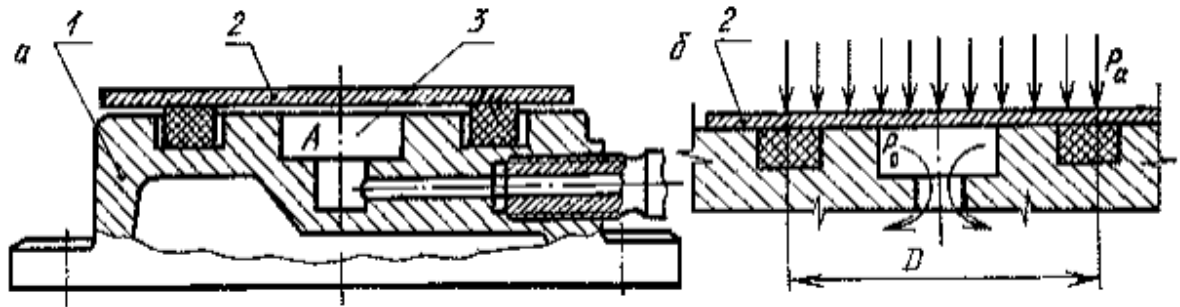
Схема вакуумного приспособления с заготовкой. В открытом (а) и прижатом (б) состояниях. 1 – приспособление, 2 – заготовка 3 – камера.
